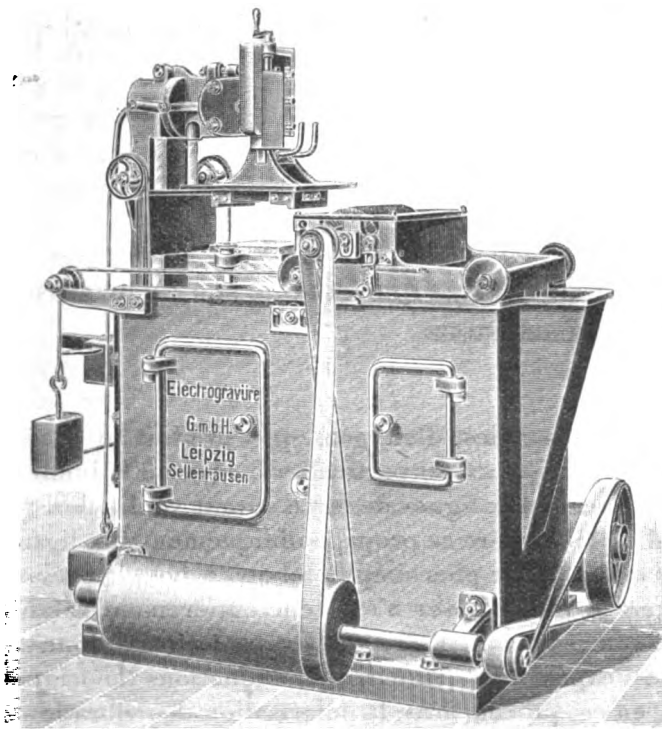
Vue d'ensemble de l'appareil Rieder.
